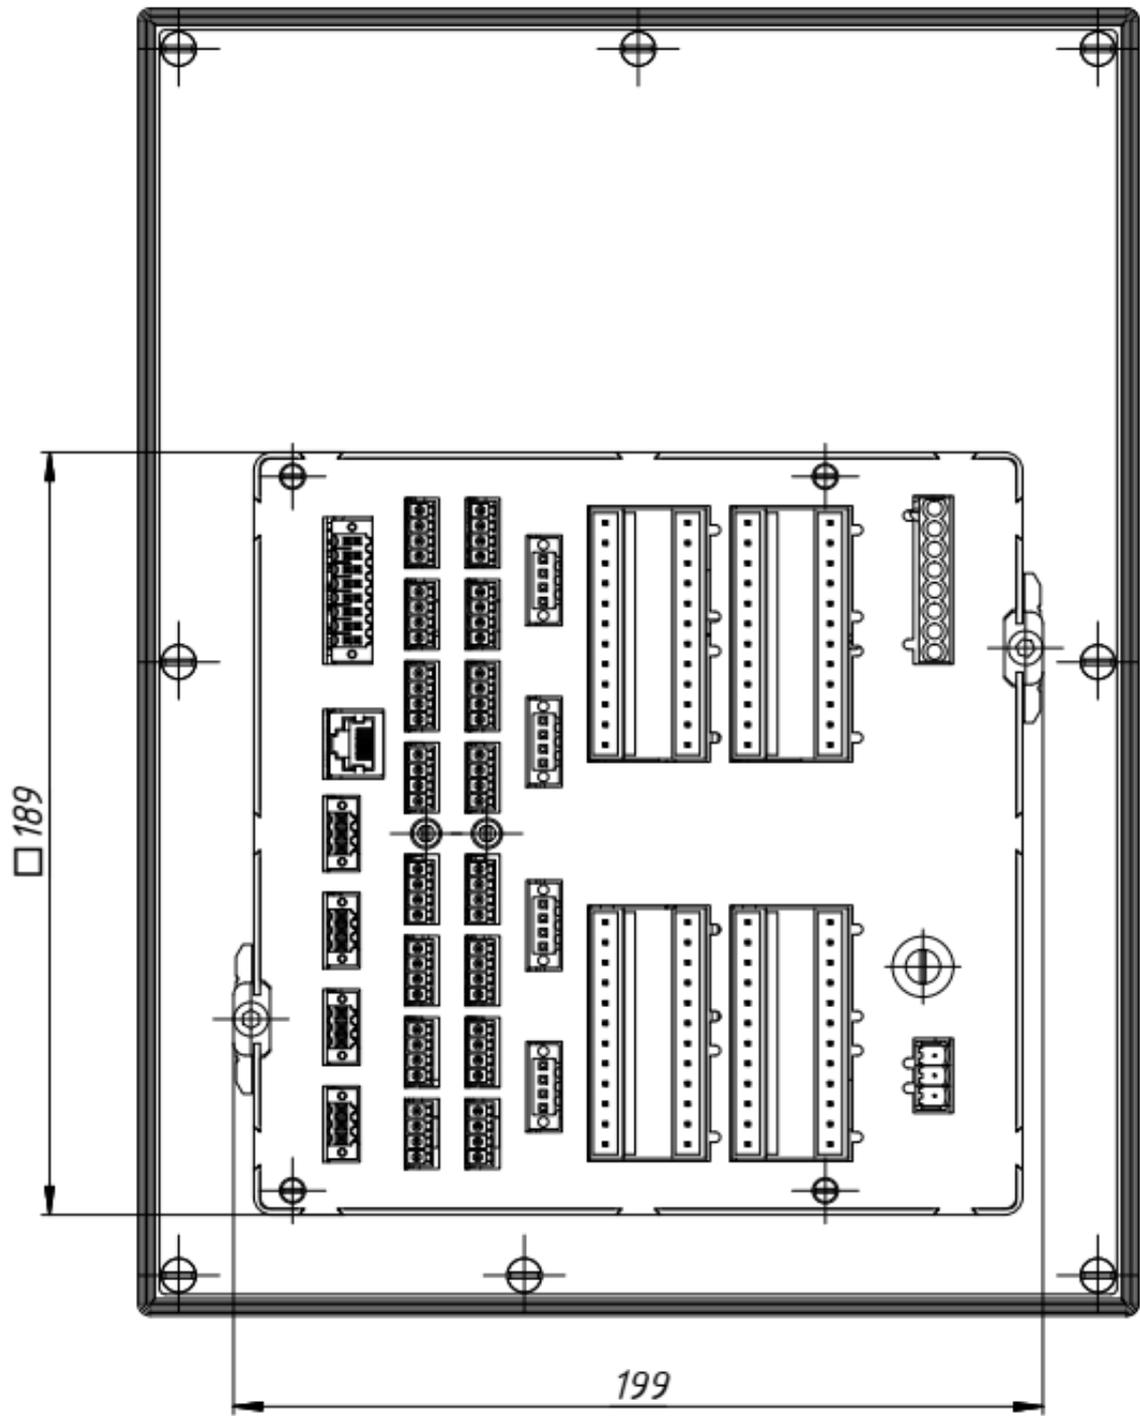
Габаритный чертёж прибора в исполнении Ф1772-2, вид сзади
